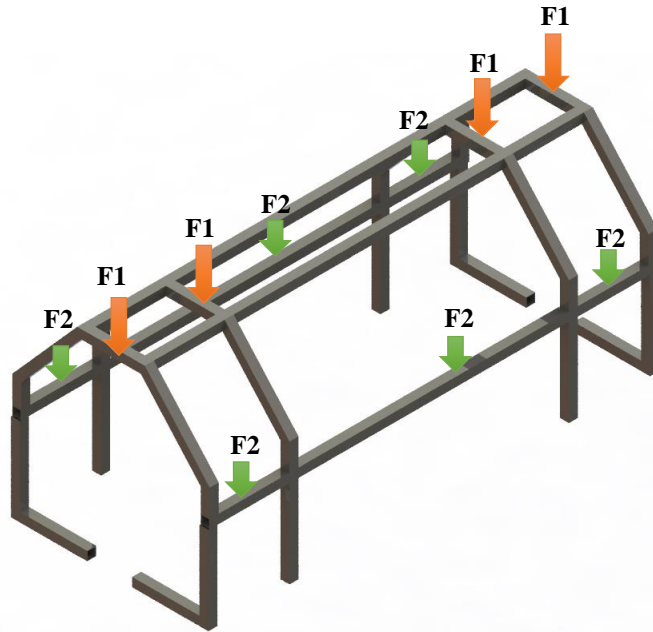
Fuerzas sobre la estructura de la cámara de despulpado.
